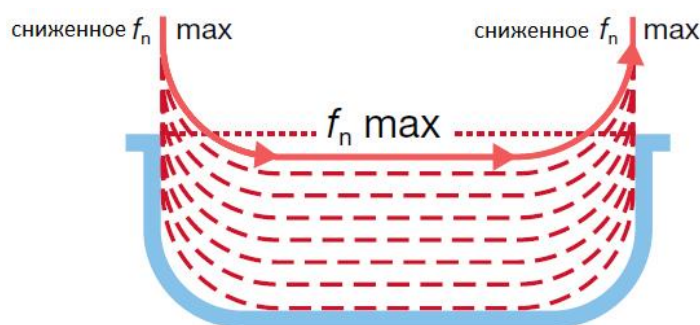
Траектории движения инструмента при черновой обработке ProfitTurning™ на токарных станках
